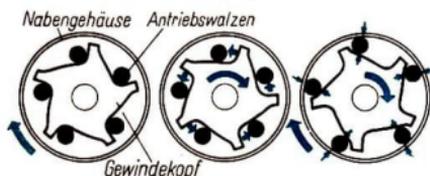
Der Gewindekopf steht still, das Nabengehäuse kann sich rechts herum frei drehen (links), der Gewindekopf beginnt sich zu drehen, die Antriebswalzen bewegen sich auf der Schräge zum Nabengehäuse (Mitte), die Antriebswalzen sind festgeklemt (rechts)
